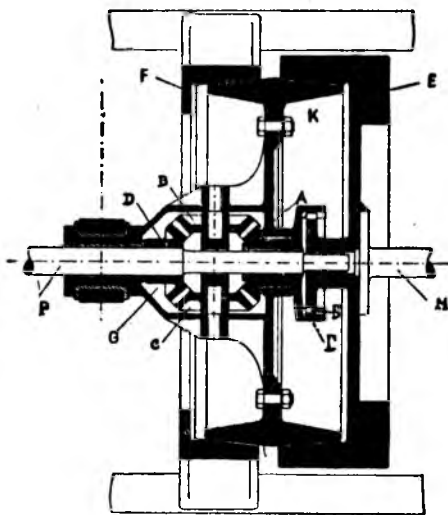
Механизм перемены вращения, с применением конических зубчаток и тормозных поверхностей. Дает передний и задний ход и промежуточное положение — разобщение. — *E*, маховик двигателя на конце коленчатого вала *M*. — *A*, коническая зубчатка, соединенная с валом двигателя. — *G*, коробка, могущая вращаться вокруг оси и соединенная с внутренним маховиком *K*. — *B* и *C*, конические зубчатки, вращающиеся на пальцах, укрепленных в коробке *G*. — *D*, четвертая коническая зубчатка, насаженная на конце гребного вала *P*. — *F*, тормоз, в который вдвигается внутренний маховик *K* для получения обратного вращения гребного вала.
